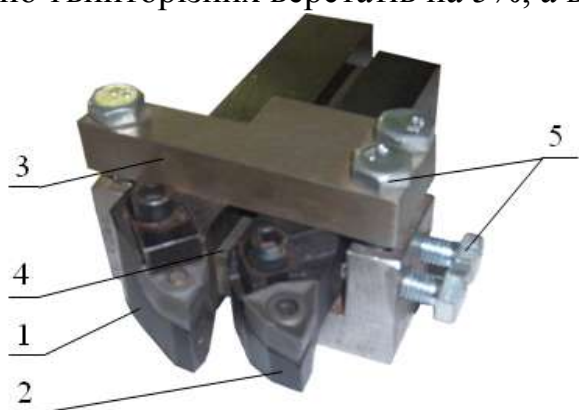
Комбінований різець (пат. України № 24137): 1 - базовий різець; 2 – різцева вставка; 3 - затискний кронштейн; 4 - прокладка; 5 - болт
